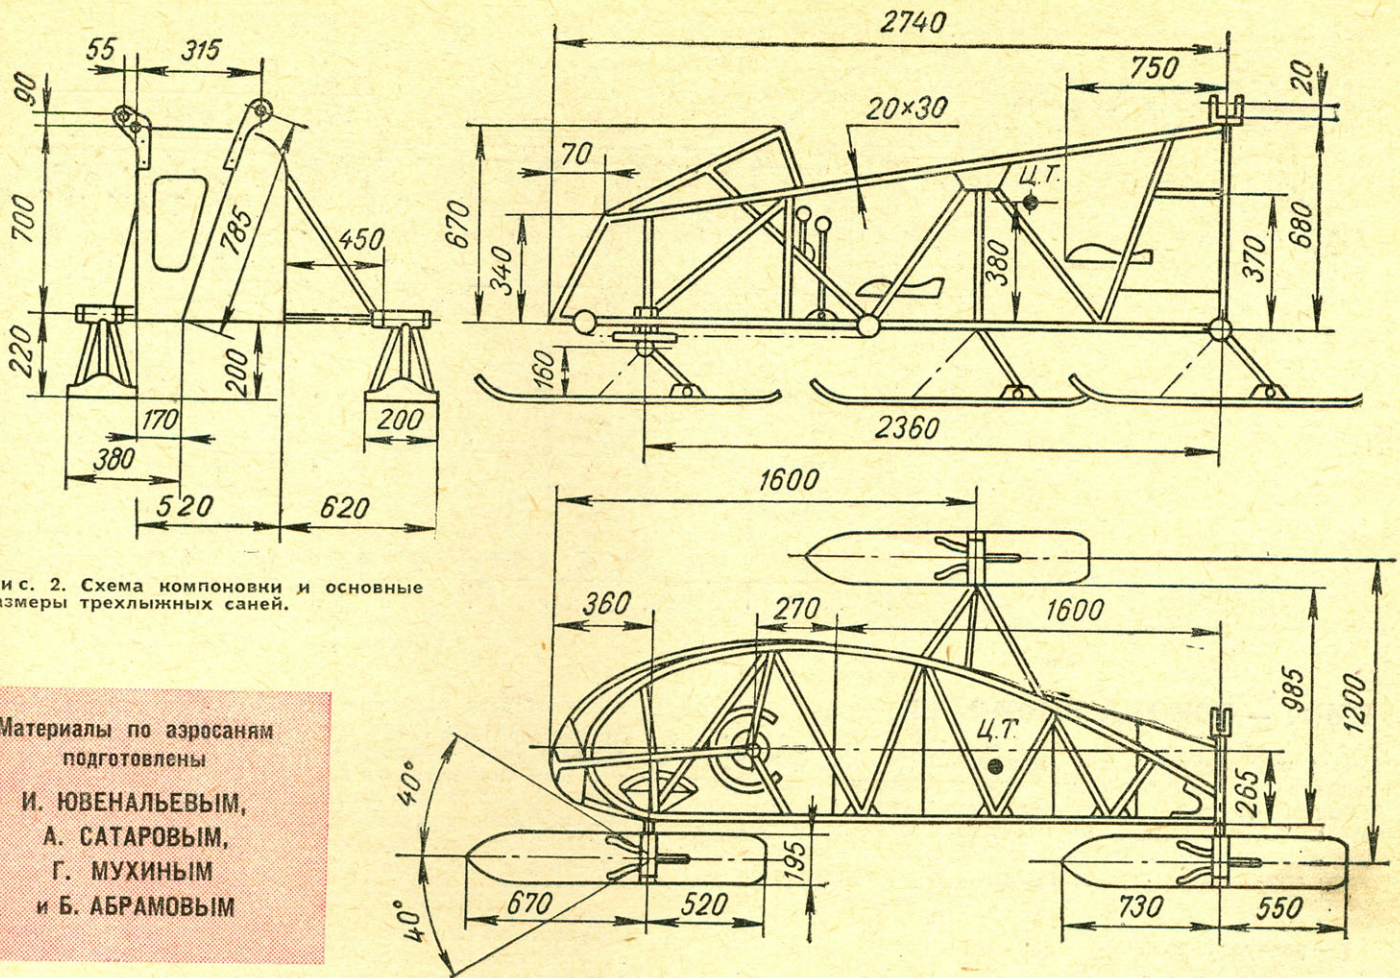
Схема компоновки и основные размеры трехлыжных саней.
